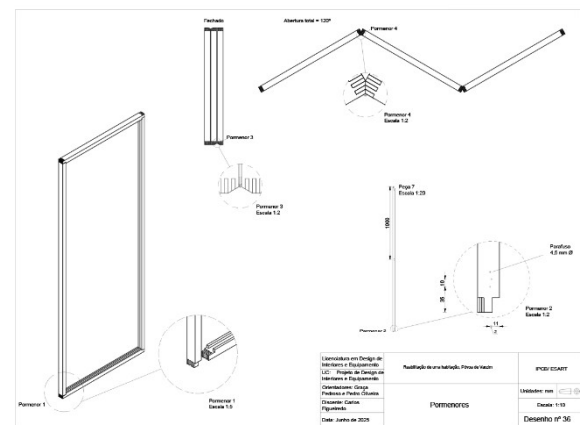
Desenho de Pormenores. Fonte: Autor.
